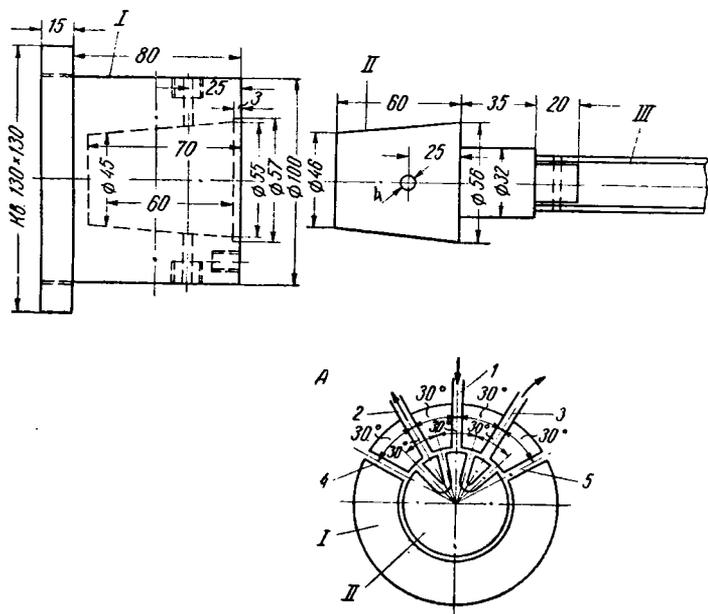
Четырехходовый клапан для распределения воздуха: I — корпус клапана; II — пробка; III — труба рукоятки для поворачивания пробки; А — поперечный разрез клапана с пробкой (при нейтральном положении пробки); 1—5 — отверстия в корпусе клапана; 1 — для поступления воздуха из компрессора; 2 — для подачи воздуха в нижнюю полость цилиндра; 3 — то же — в верхнюю полость; 4 — для выпуска воздуха из нижней полости цилиндра; 5 — то же — из верхней полости
